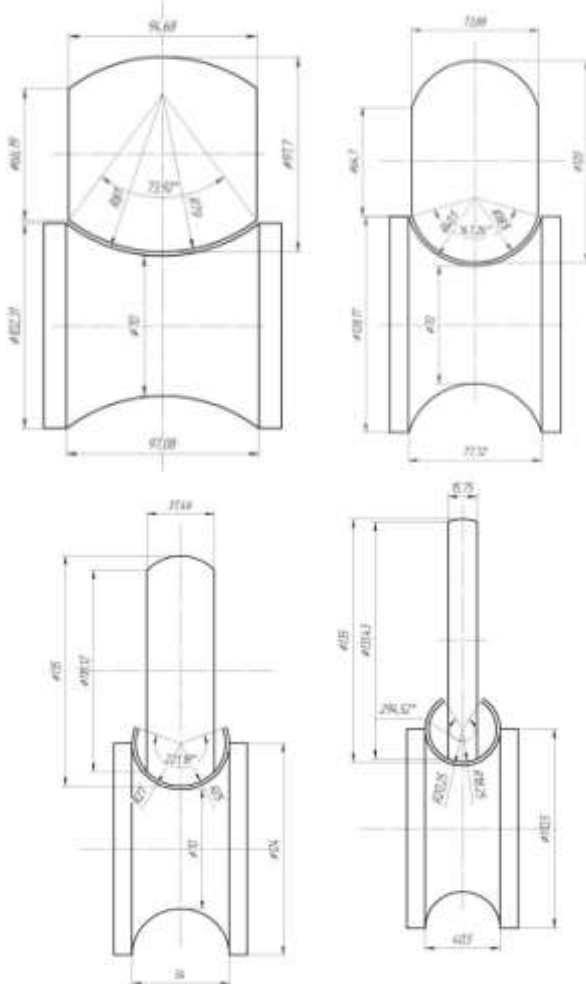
Комплект инструмента для трубы типоразмером 30x1
